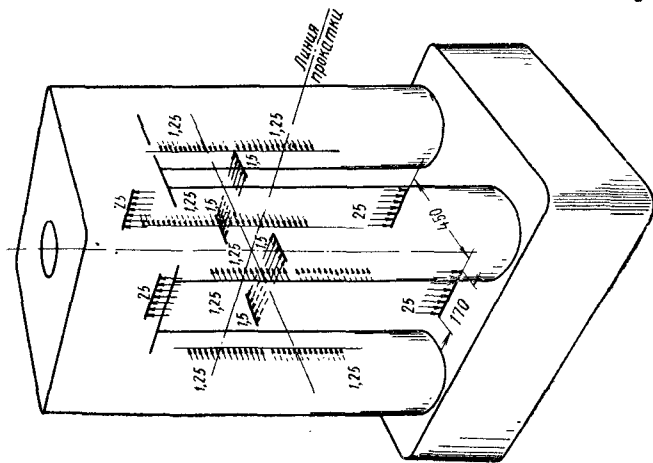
Конструкция стального каркаса железобетонной клетки стана «Кварто-200».
